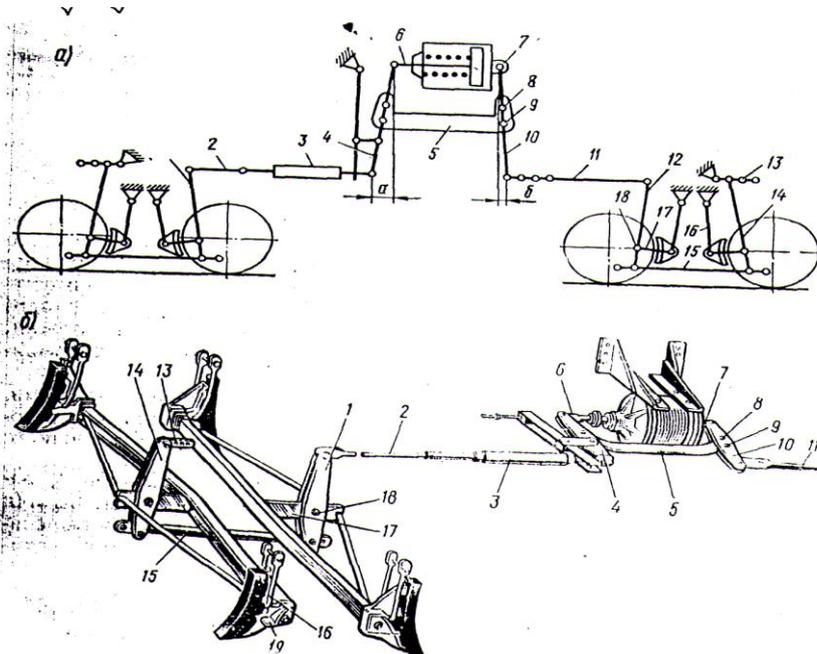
Схема (а) и конструкция (б) рычажной передачи четырехосного вагона.
